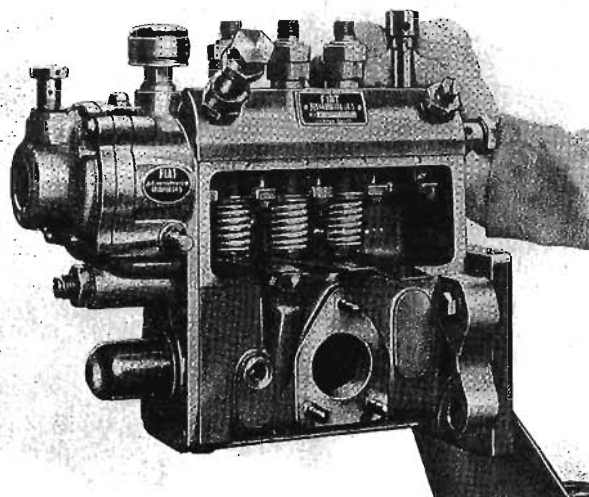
Smontaggio e rimontaggio dei cilindri.
